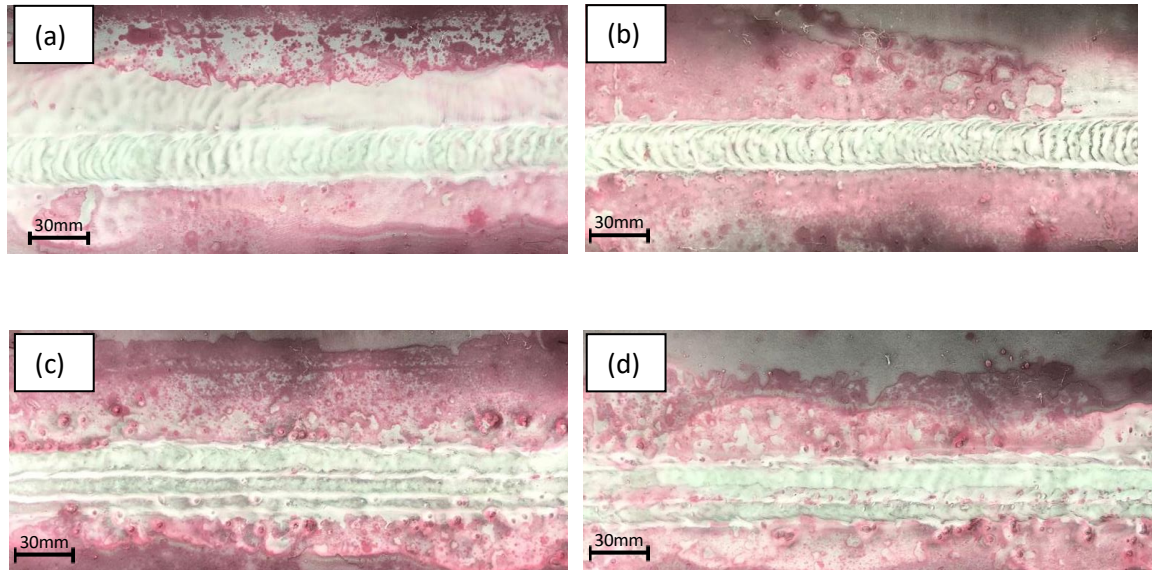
Ensaio de Líquidos Penetrantes dos diferentes conjuntos soldados a) Com tecimento (C1), b) Com tecimento (C2), c) Filetado (F1), d) Filetado (F2).
